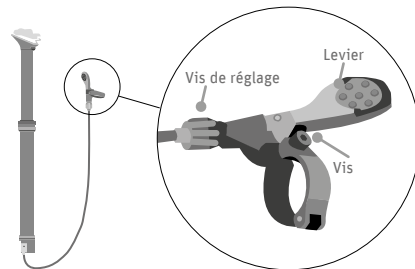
Tige de selle télescopique Fig. 21 Module de commande
